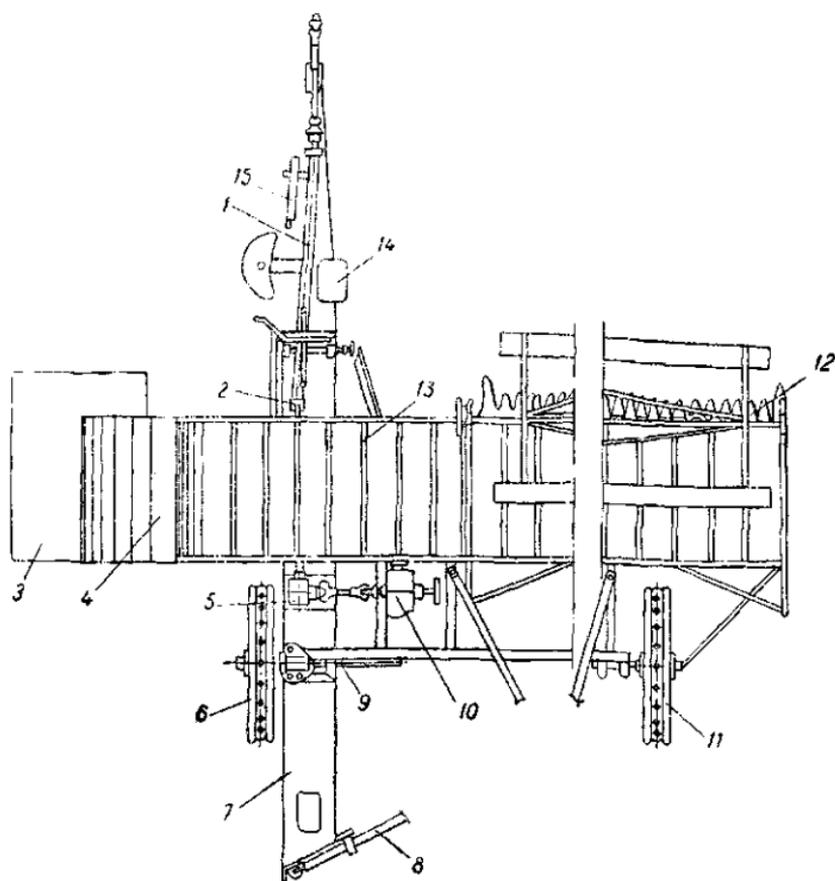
Схема рядковой жатки (виндрузера) ЖР-4,9 в рабочем положении:
